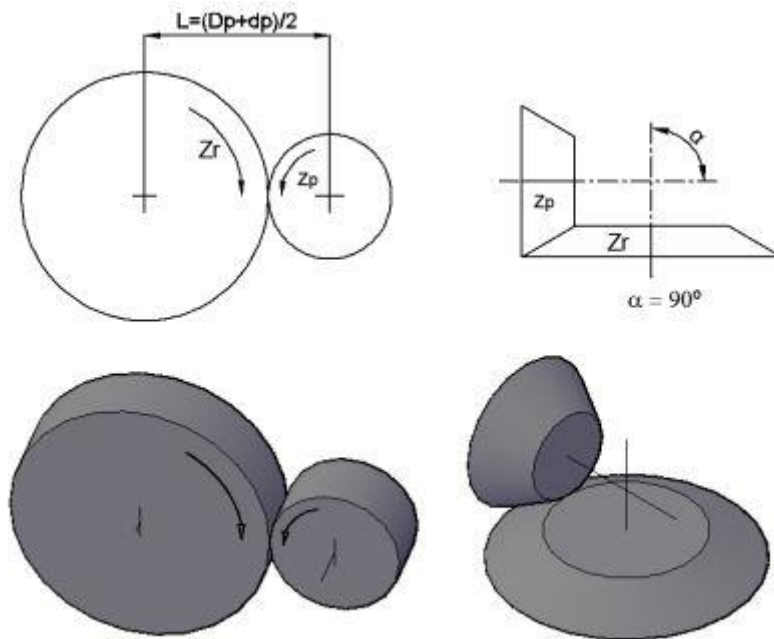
Engranajes con ejes paralelos y ejes perpendiculares. [28]
